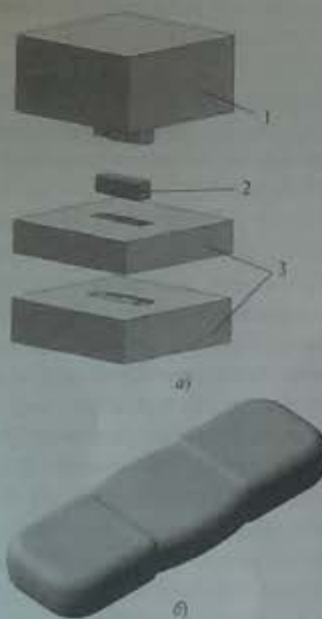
Закрытый штамп с заготовкой (а) и модель поковки, полученной в закрытом штампе (б). 1 — пуансон, 2 — заготовка, 3 — матрица
